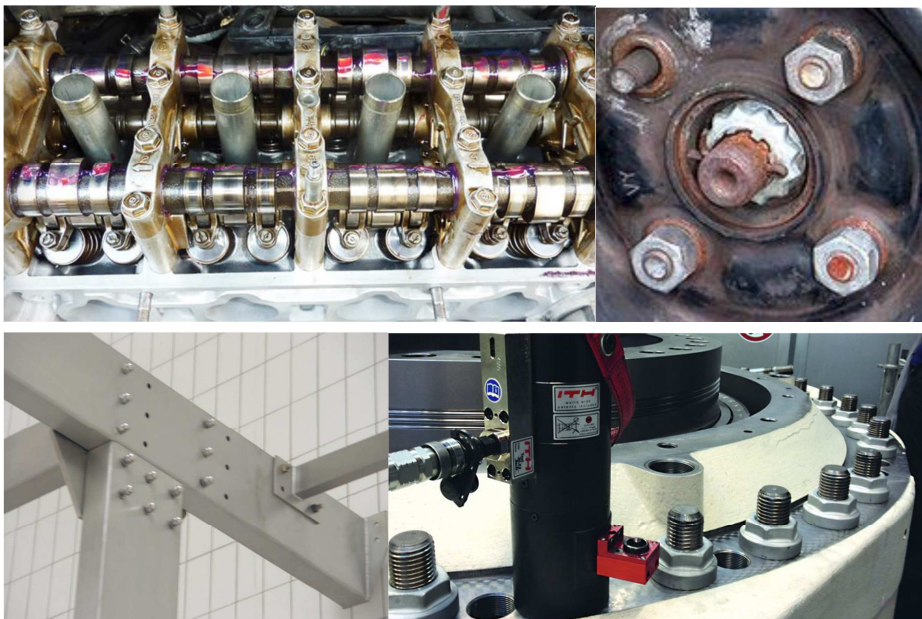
Spajanje metalnih konstrukcija zakovicama<sup>65,66</sup>
